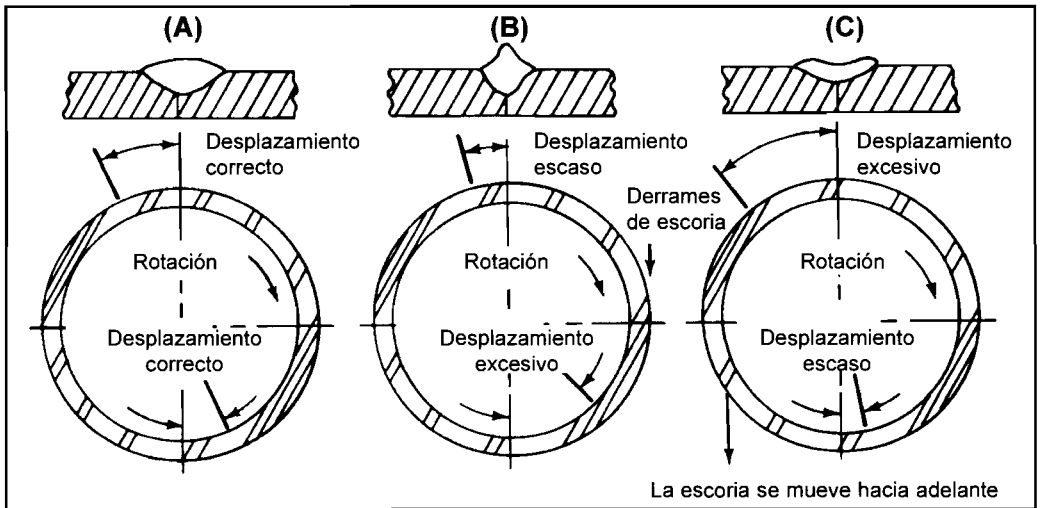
EFECTO DE LAS POSICIONES DEL ELECTRODO SOBRE LA FORMA DEL CORDÓN DE SOLDADURA DURANTE EL SOLDEO CIRCUNFERENCIAL
